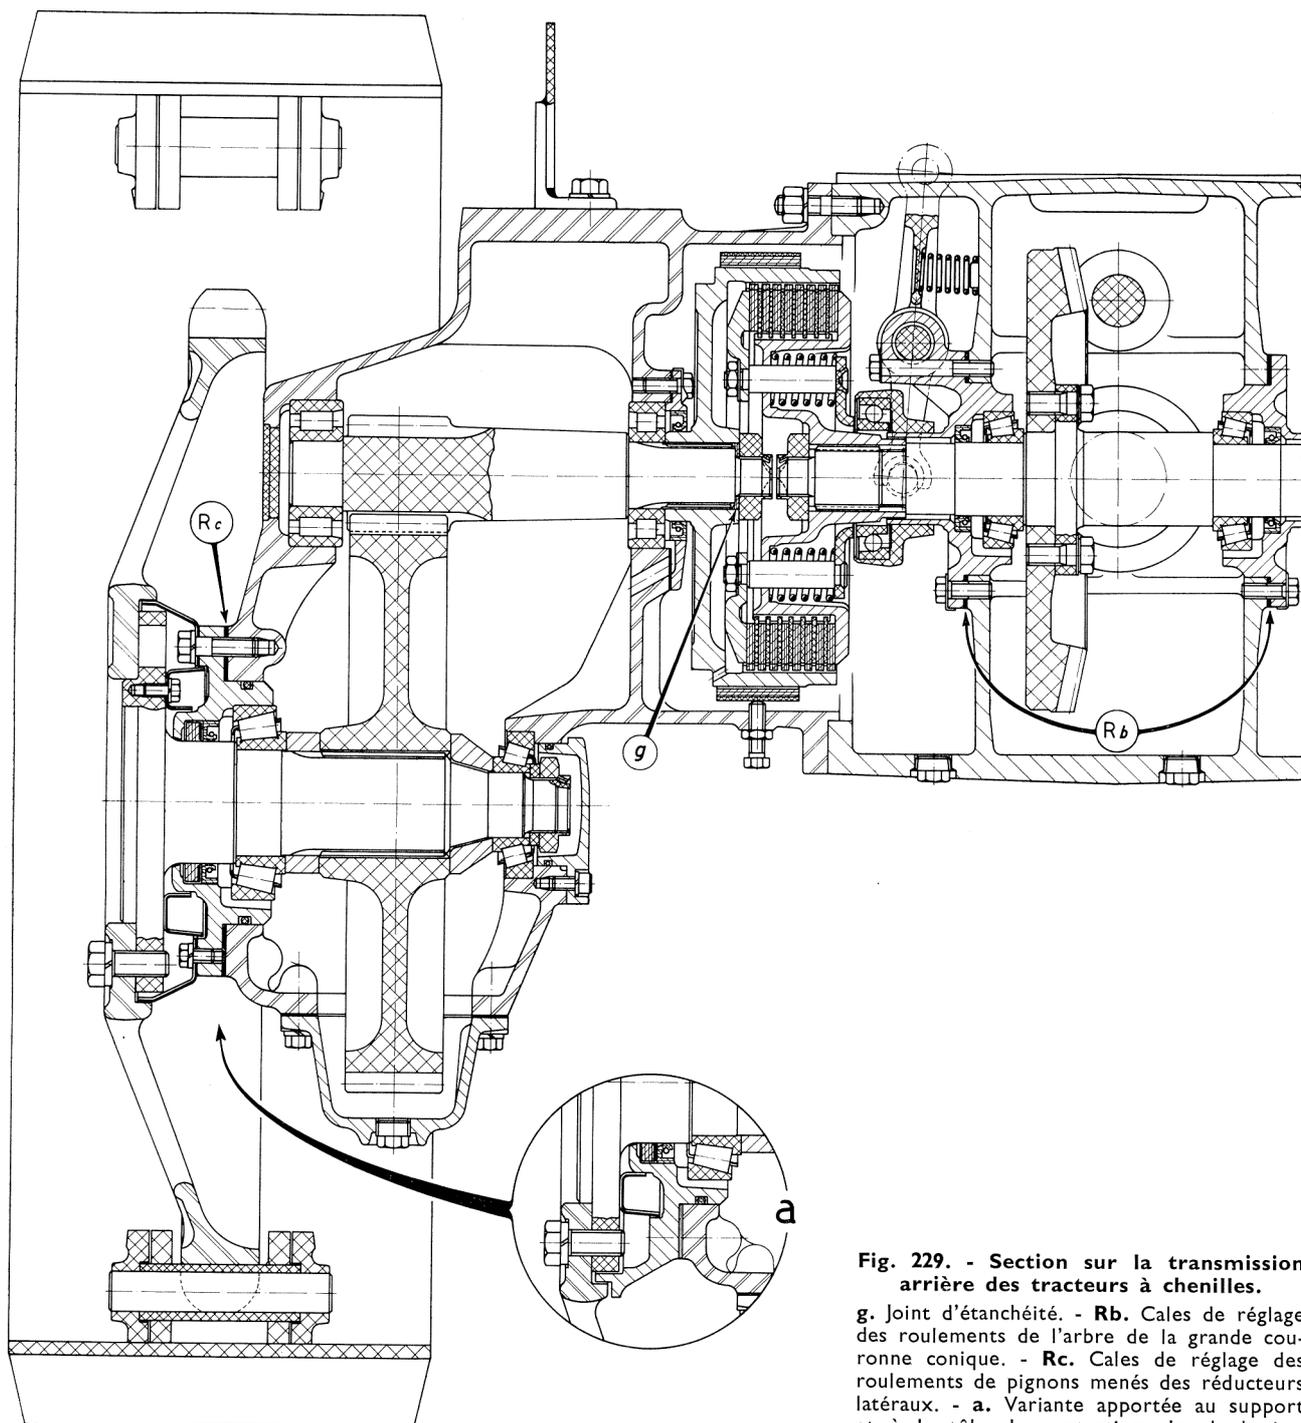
Section sur la transmission arrière des tracteurs à chenilles.
